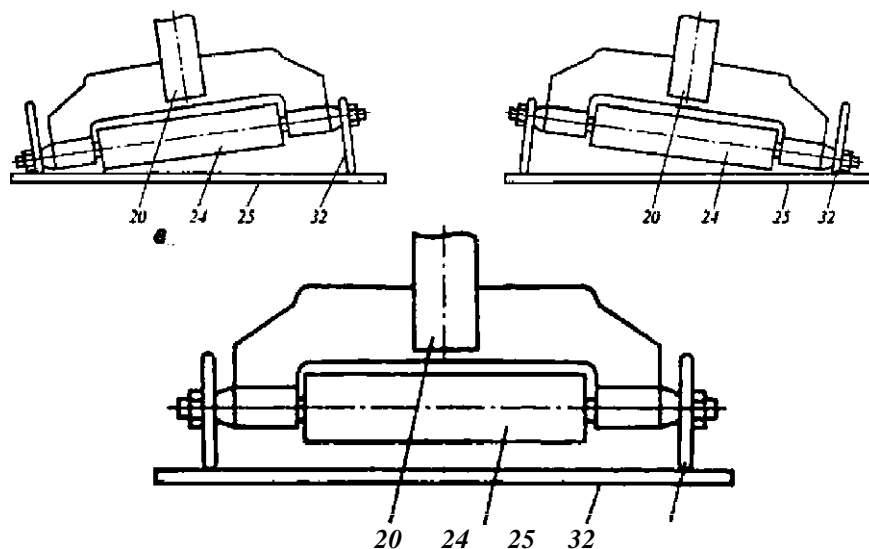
Положение ползуна с роликом при снятии бокового наката с крестовины (а, б) и при шлифовке крестовины станком 2152
